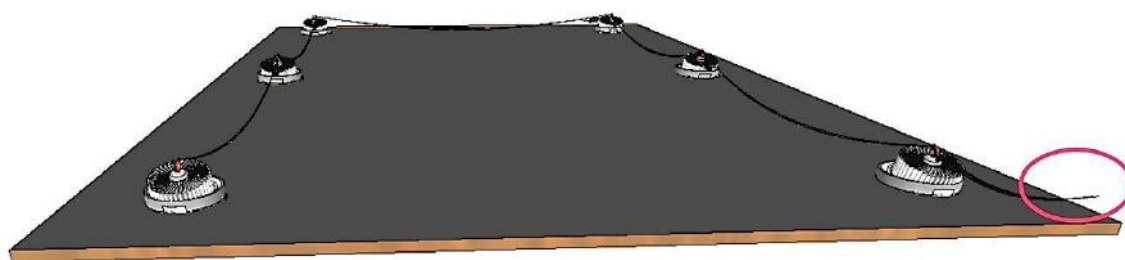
Tampa que fecha a *Base da Plataforma* vista por dentro com destaque em rosa do ponto que a fiação sairá para dentro do *Conjunto Torre* (Fonte: elaboração própria).
